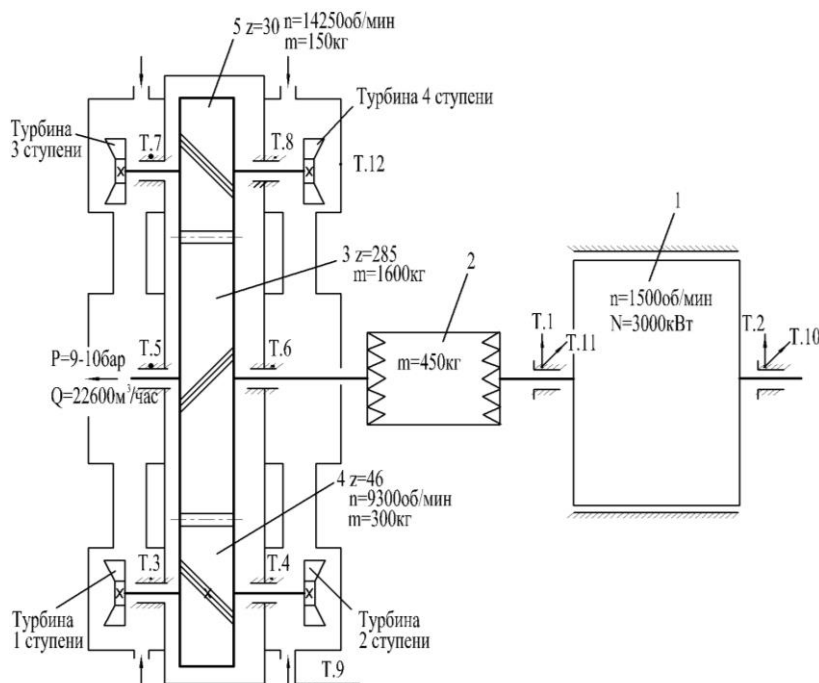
Кинематическая схема компрессора «DEMAG»:
